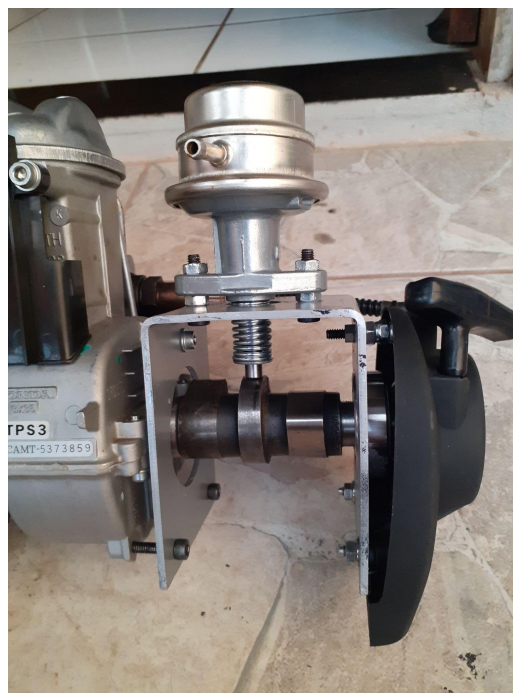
Suporte para fixação da bomba de combustível no motor
